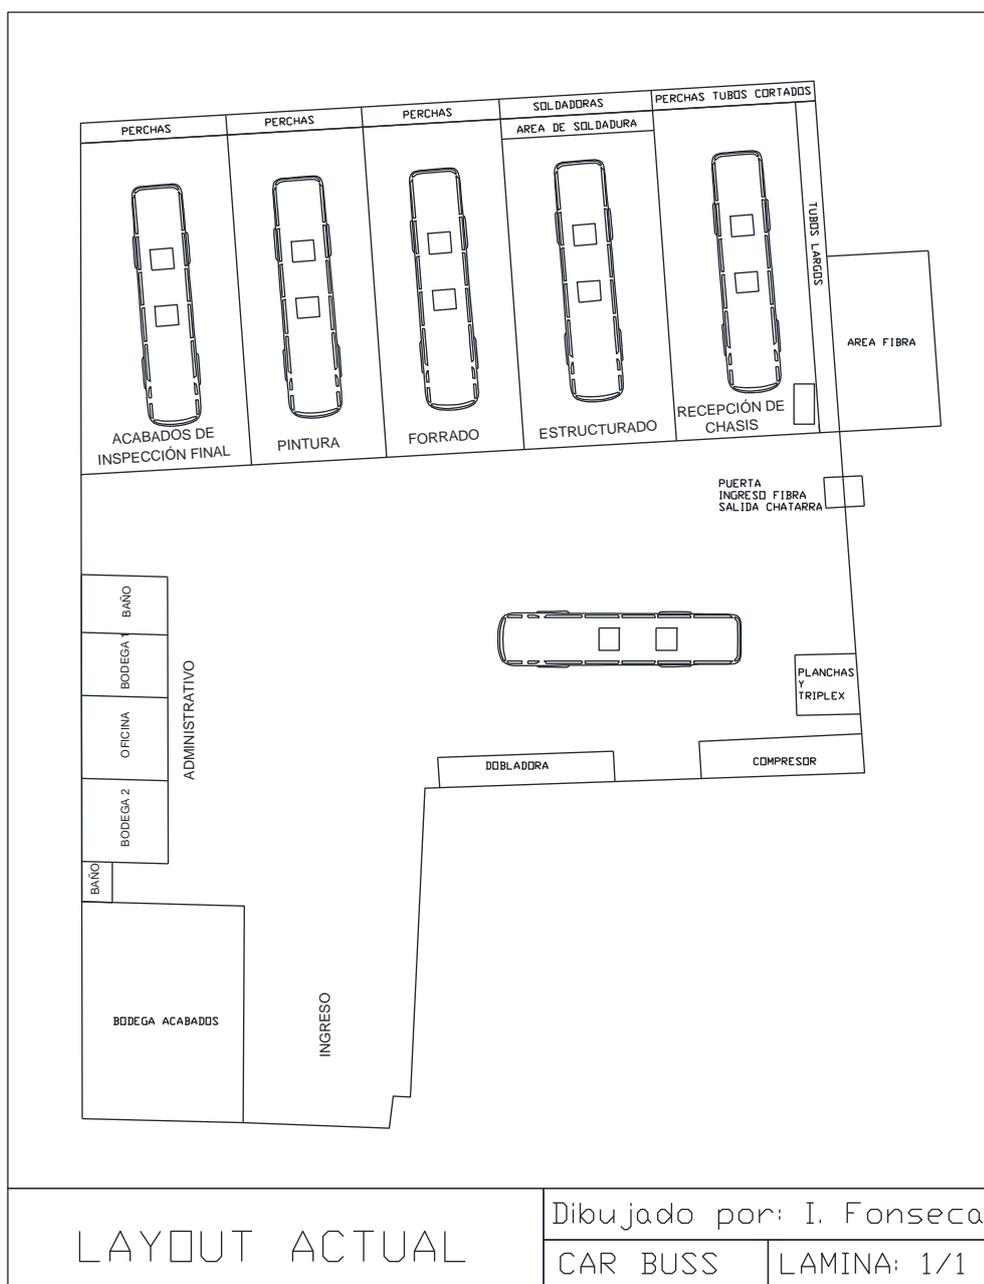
Layout de la empresa Car Buss Yaulema.
